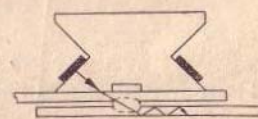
Схемы прозвучивания сварной точки.
